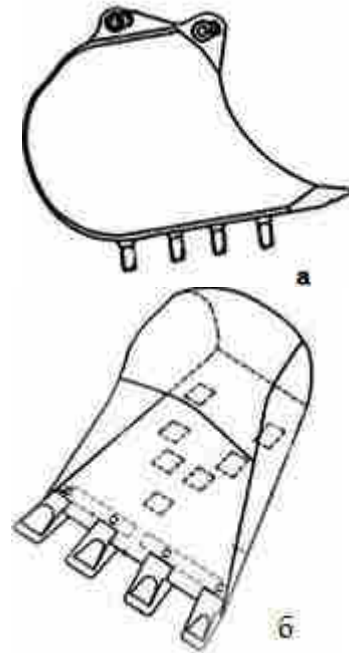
Совкоподібний ківш: а – розстановка розпушувальних зубів на днищі ковша, б – зображений загальний вигляд робочого органу [13]
